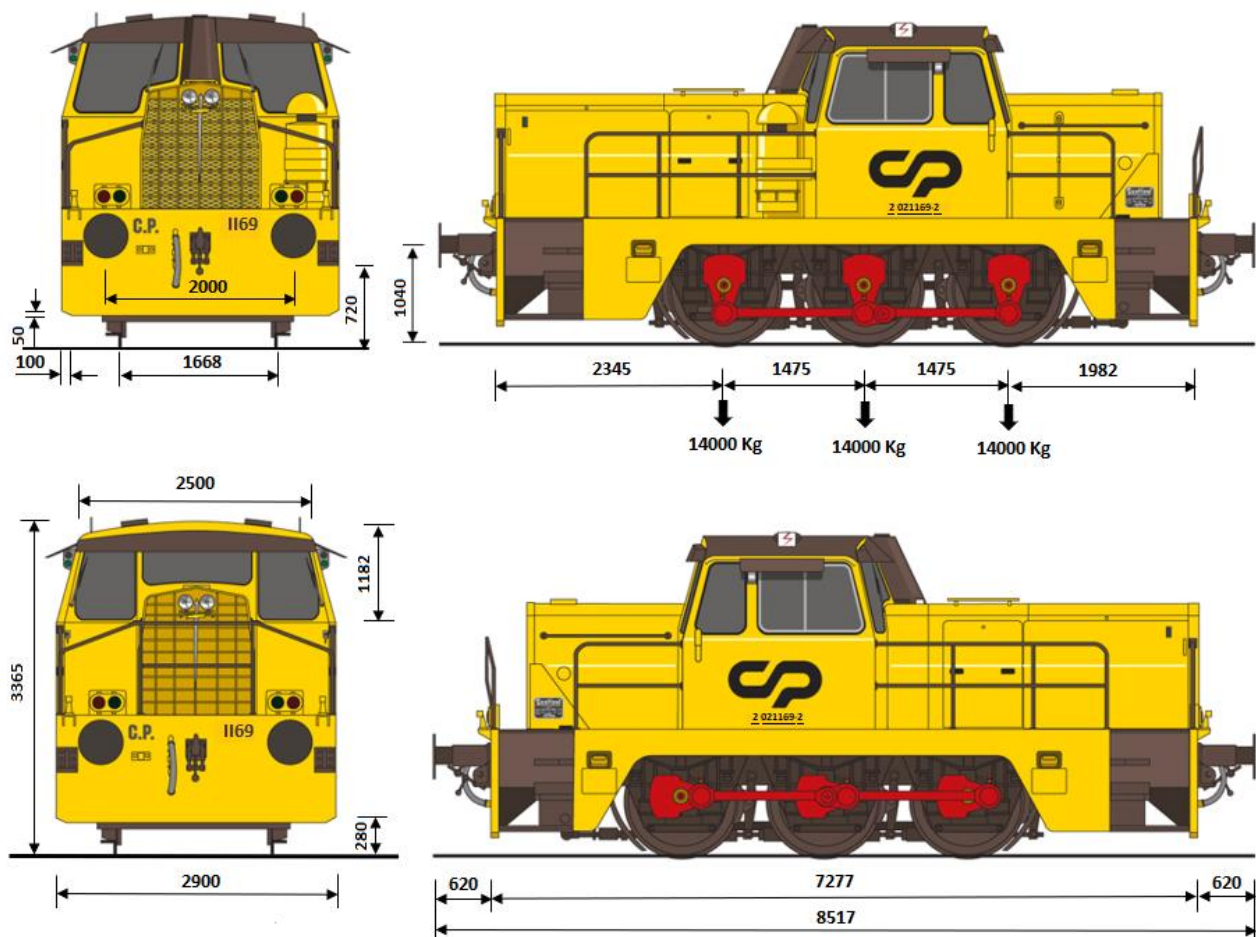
Desenho com dimensões do locotrator Sentinel n°1169, adaptado de [41]
